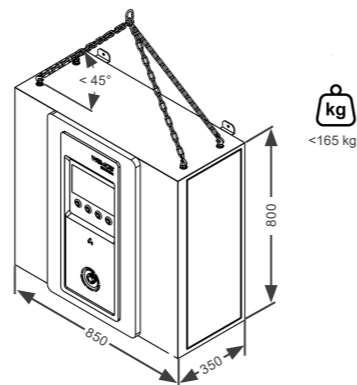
Geometría, masa e izamiento recomendables para la WEMOB-STATION - mm
